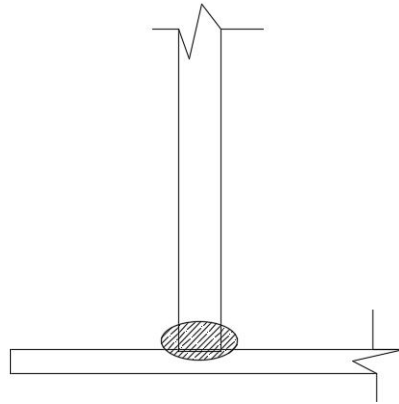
Unión Manto-Fondo Soldada. [5]
